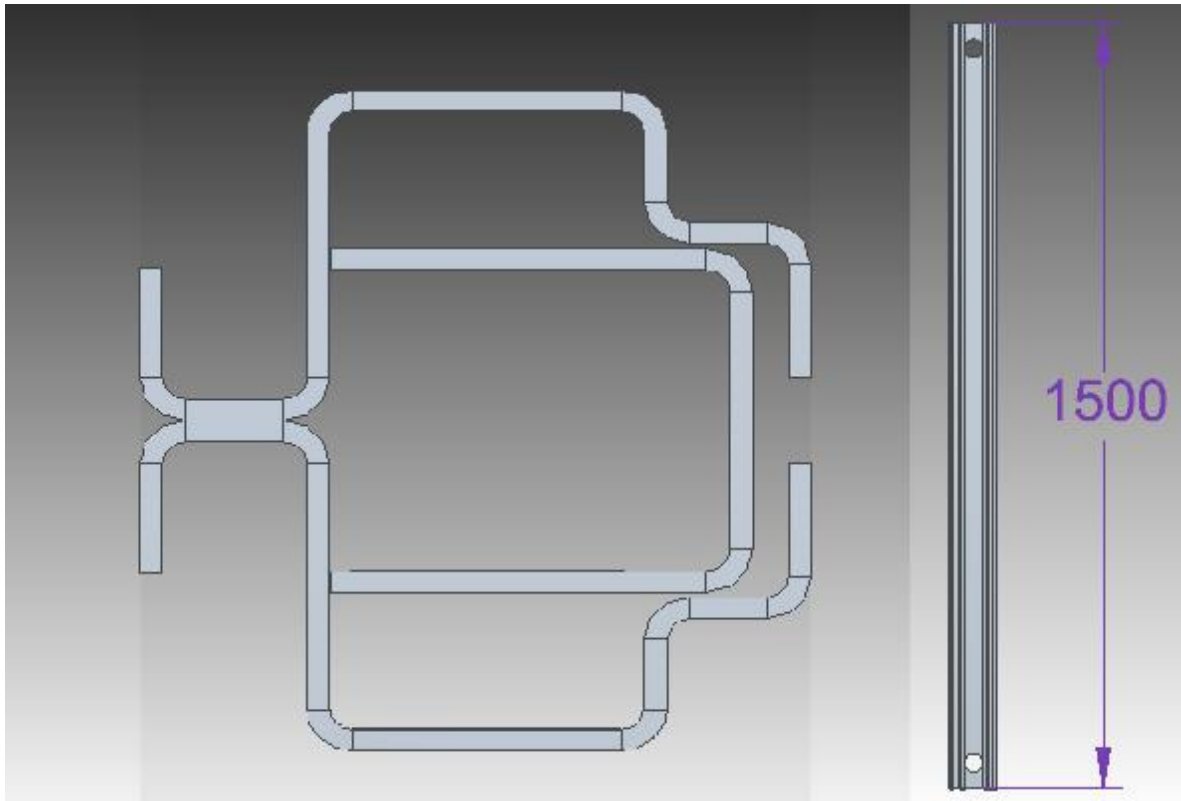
Diseño de la segunda sección de la torre hecha con lamina de acero doblada.
